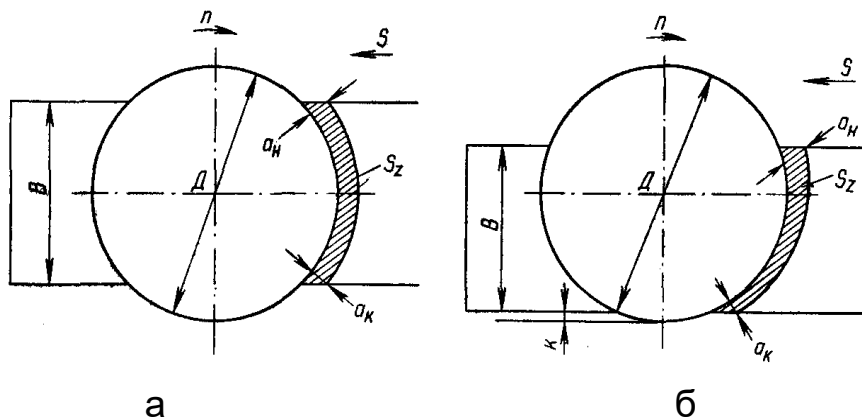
Схемы симметричного (а) и несимметричного (б) торцового фрезерования
